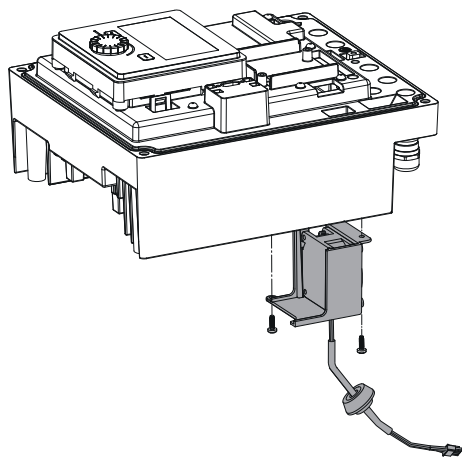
Retirar o ventilador do módulo, incluindo o cabo e o vedante de borracha
